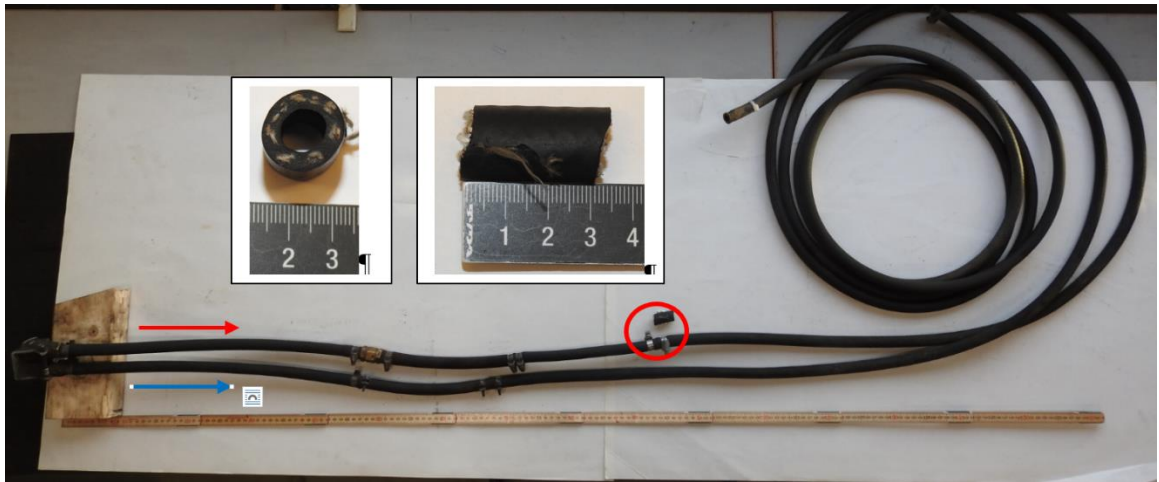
Sammenkobling av komponenter mellom lastebil og tilhenger. Rød sirkel viser området på slangen hvor det oppsto luftlekkasje. Rød pil viser festebrakett til underkjøringshinderet på lastebilen. Foto og illustrasjon: SHK
